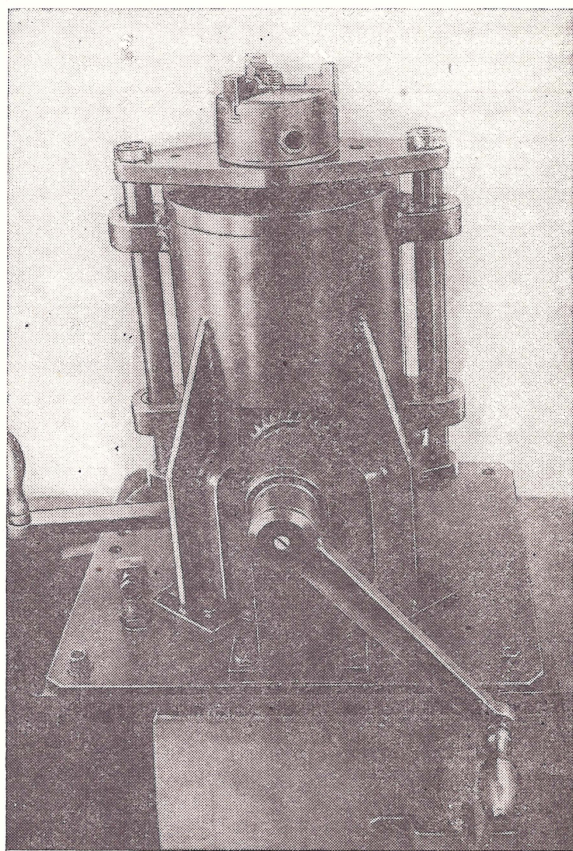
Общий вид завивочной машины ВНИИ (лабораторный тип)
